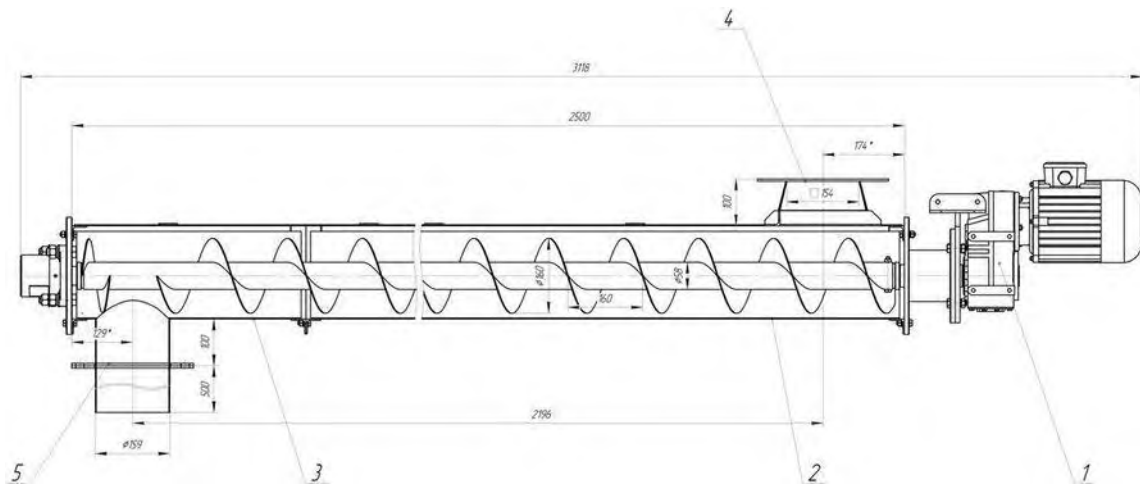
Загальний вигляд, компоновка та основні конструктивні елементи гвинтового конвеєра KB-320. 1 – *мотор-редуктор*, 2 – *корпус*, 3 – *шнек*, 4 – *вхідний патрубок*, 5 – *вихідний патрубок*.
